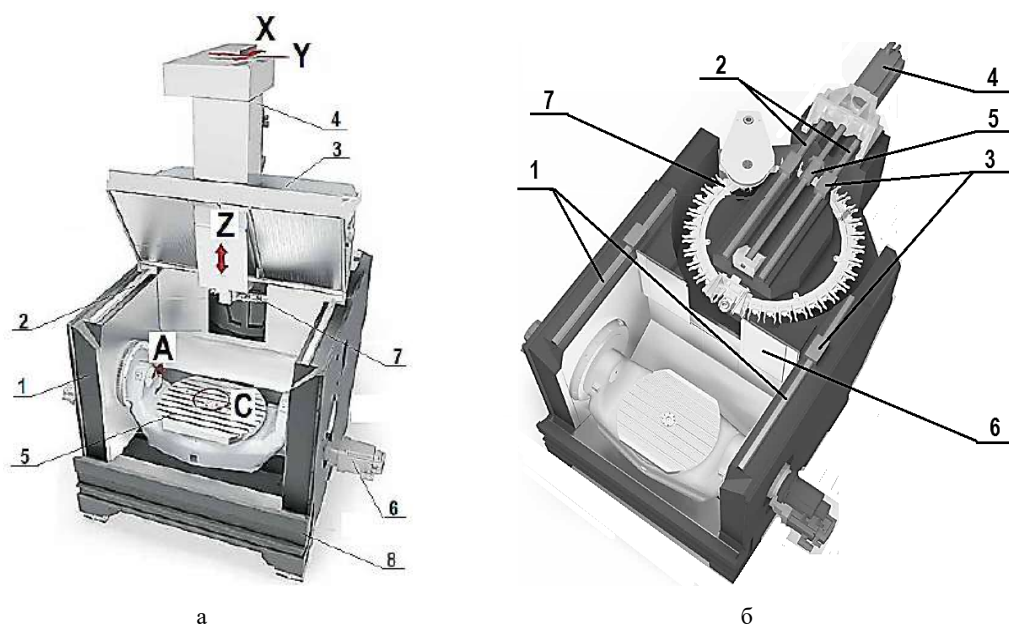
Верстат Hermle C42: а - координатні осі верстата; б – розташування інструментального магазина
